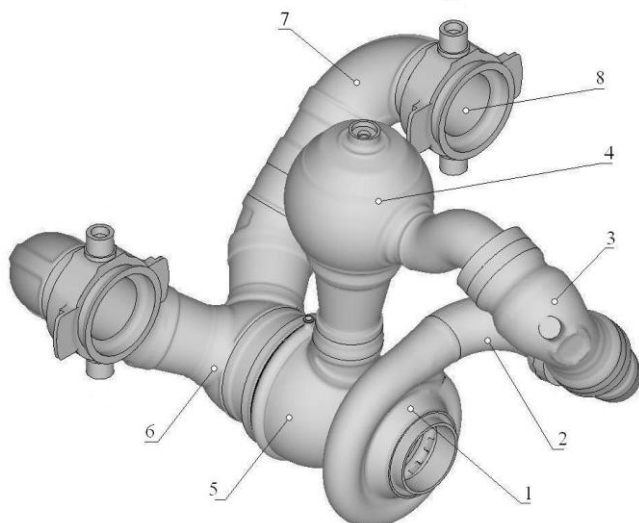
Вид под сборки двигателя РД180: 1 – корпус насоса окислителя; 2 – кислородная магистраль высокого давления; 3 – главный клапан окислителя; 4 – газогенератор; 5 – статор турбины; 6 – выхлопной коллектор; 7 – газовод; 8 – опорный пояс
